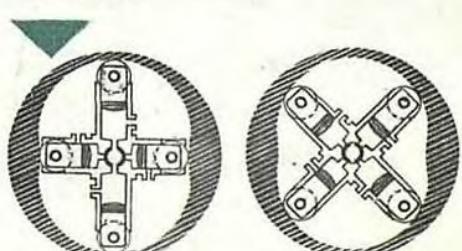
Двигатель Меркера. Крестообразный блок цилиндров, в котором ходят поршины, оканчивающиеся роликами, вращается внутри корпуса со своеобразной поверхностью вокруг впускной трубы с прорезями, служащей цилиндрическим золотником. Для выпуска служат окна (двигатель работает по двухтактному циклу).
